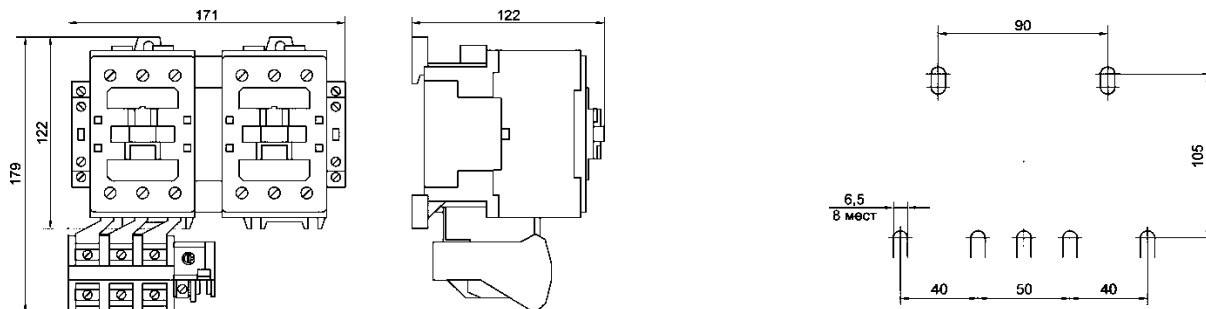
Пускатель реверсивный ПМ12-063 63А. Степень защиты - IP20
